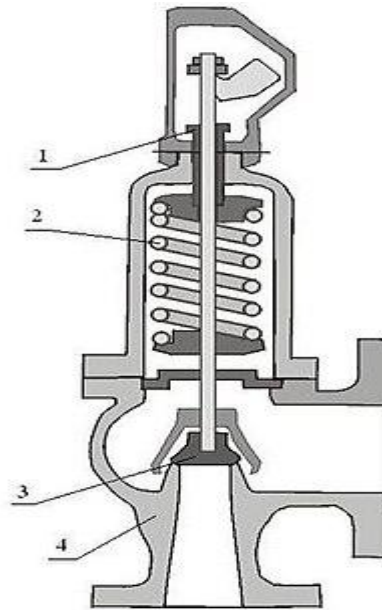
Будова запобіжного клапана: 1 — гвинт; 2 — пружина; 3 — золотник; 4 — корпус.
